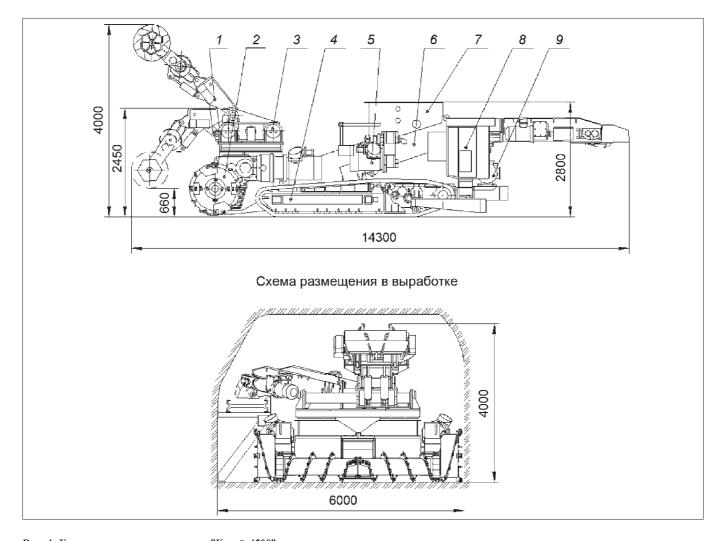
Конструктивная схема машины "Калий-4500": I — исполнительный орган; 2 — бермовый орган; 3 — механизм поперечного перемещения исполнительного органа; 4 — гусеничный ход; 5 — насосная станция; 6 — конвейер; 7 — гидросистема; 8 — кабина; 9 — электрооборудование
